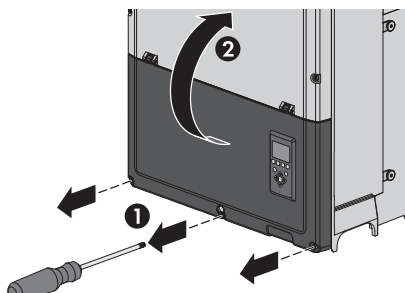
Afloje los tornillos y levante la cubierta del área de instalación.
